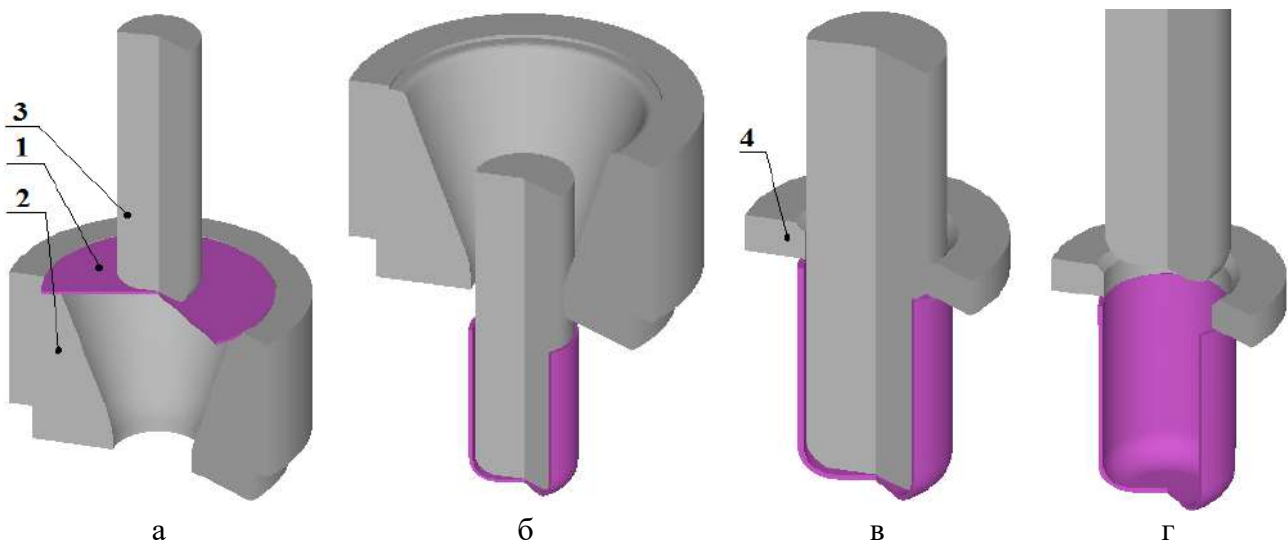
Розрахункові положення заготовки і деформуючого інструмента:
